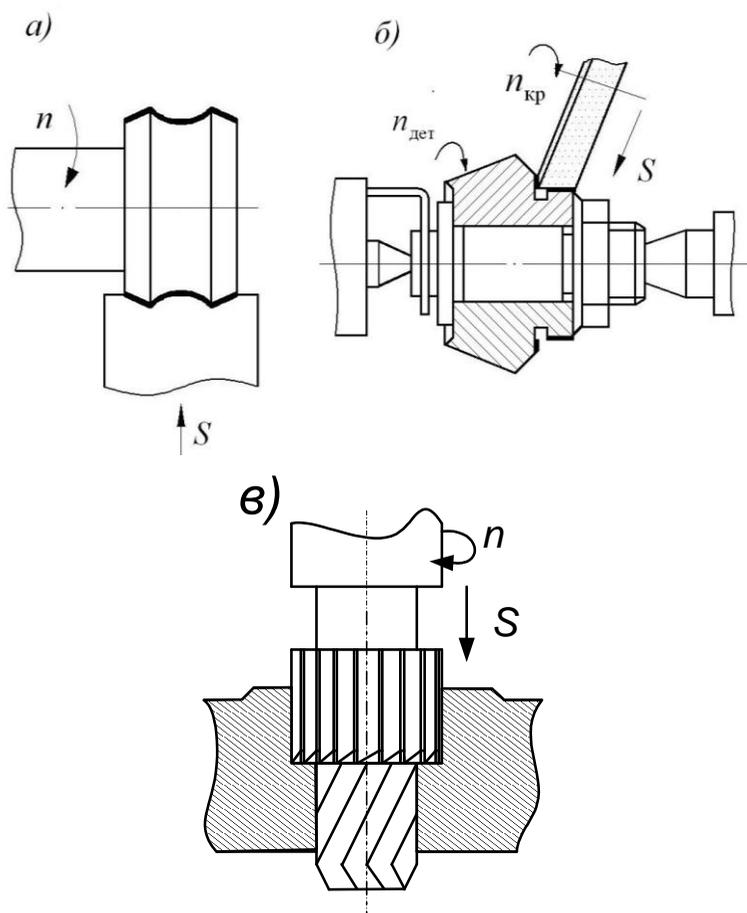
Примеры параллельной обработки нескольких поверхностей одной детали сложными инструментами:
